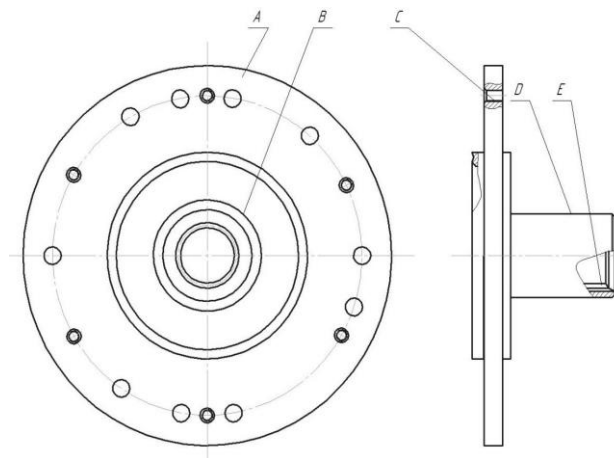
Фланець ведучої частини маточини колеса
